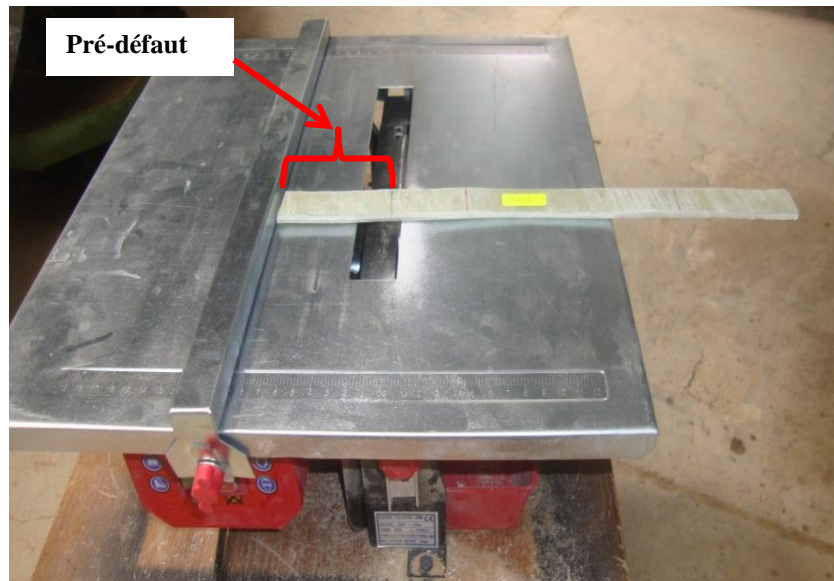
Découpage et préparation des éprouvettes DCB.
